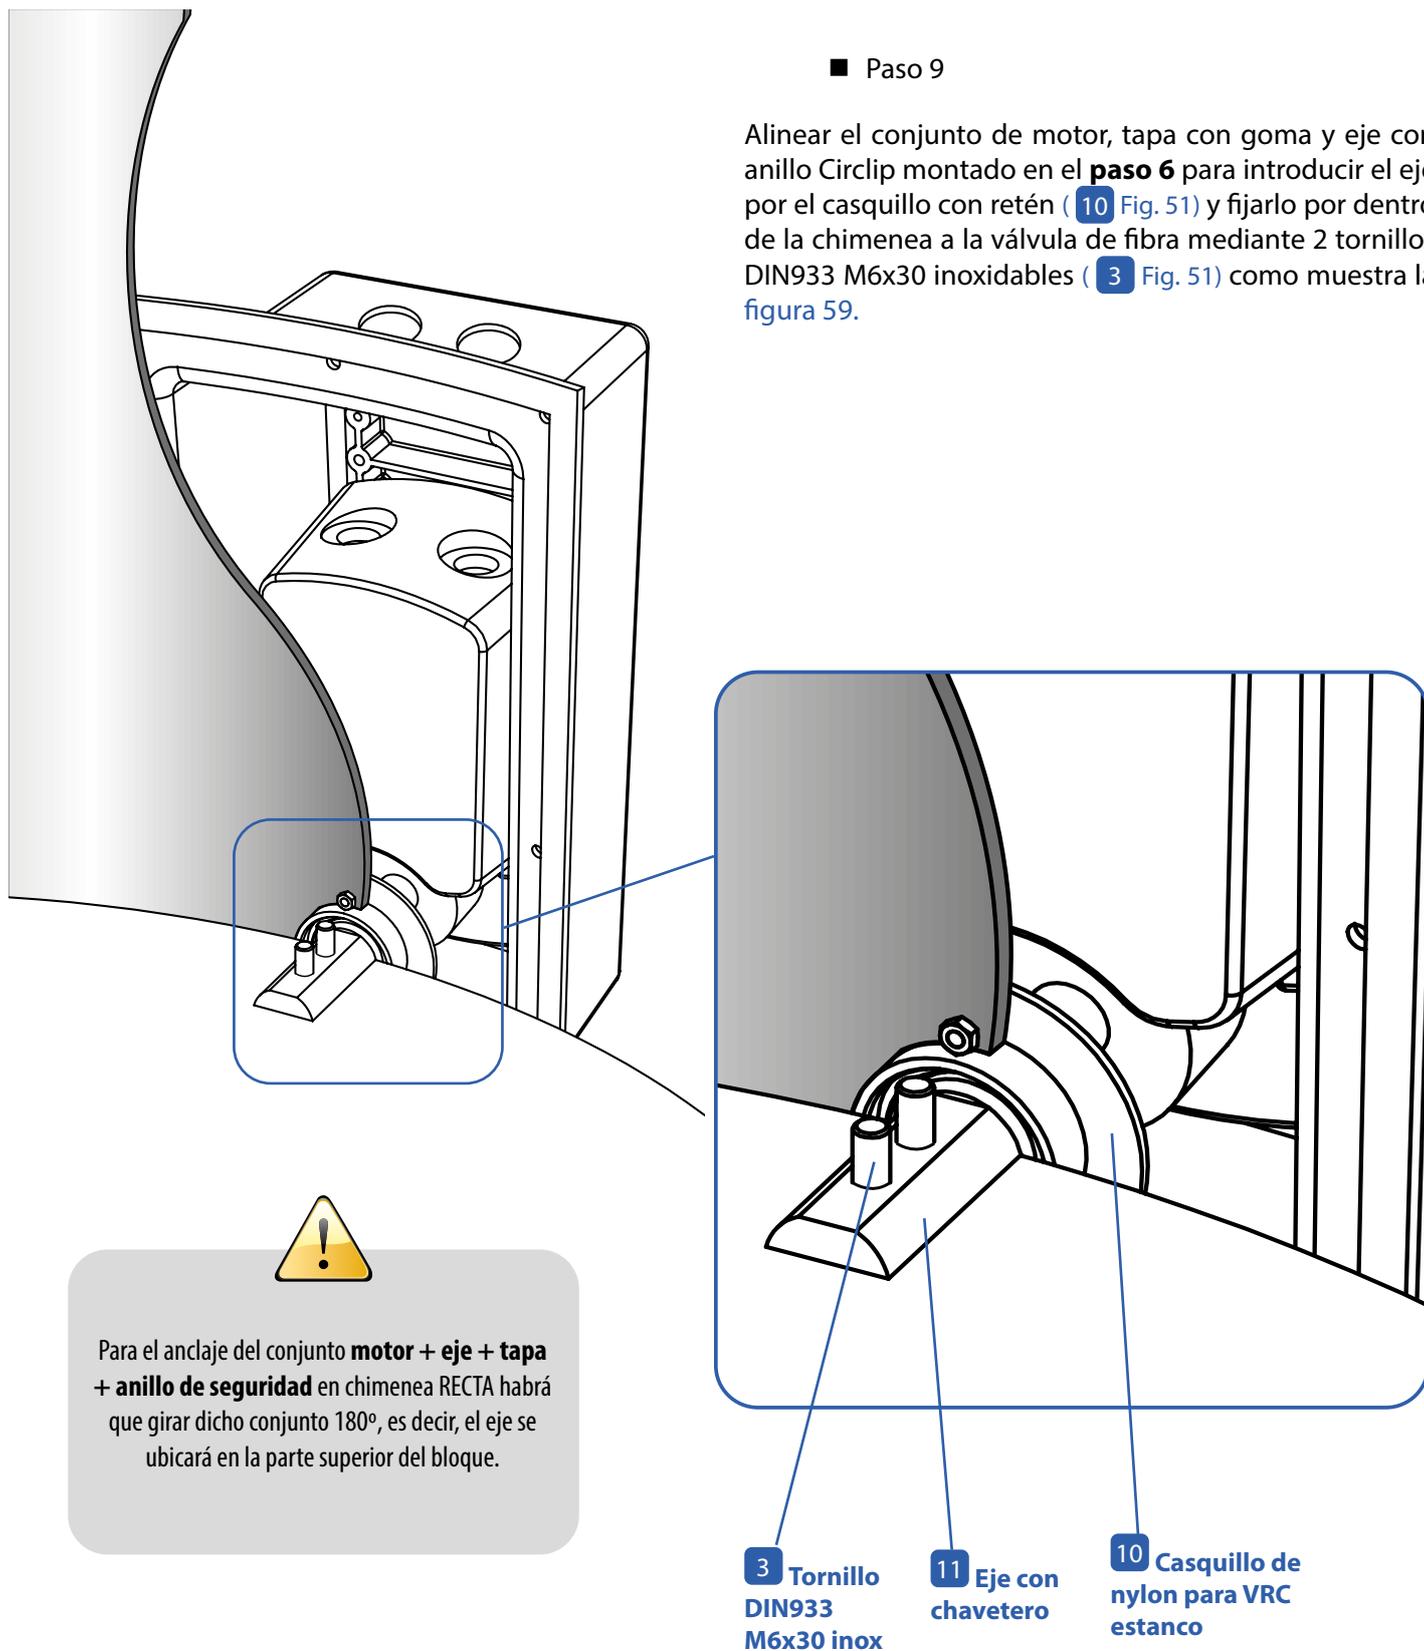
Anclaje del conjunto motor en la válvula para chimenea CÓNICA.
